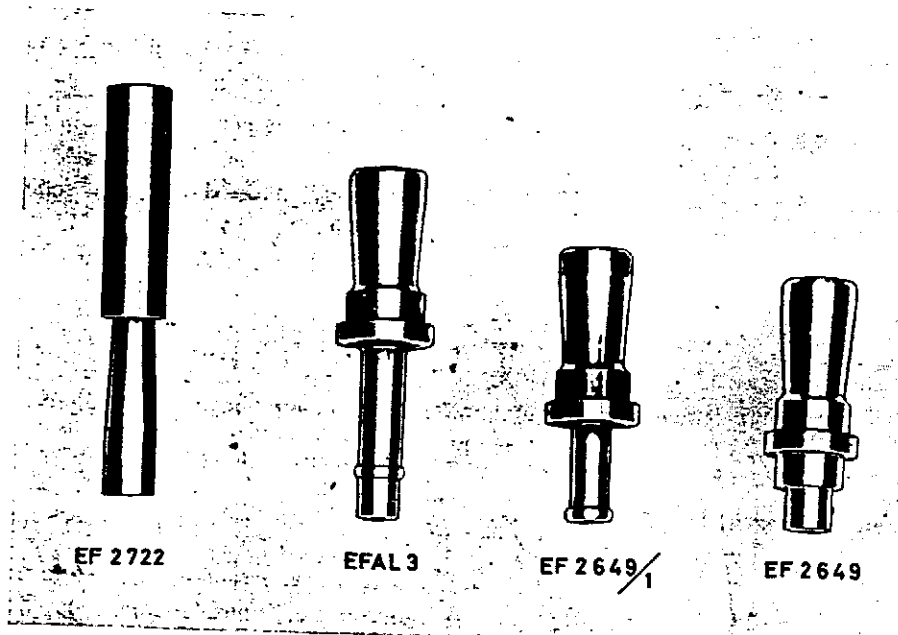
Bosch-Spezialwerkzeuge für Anlasser
